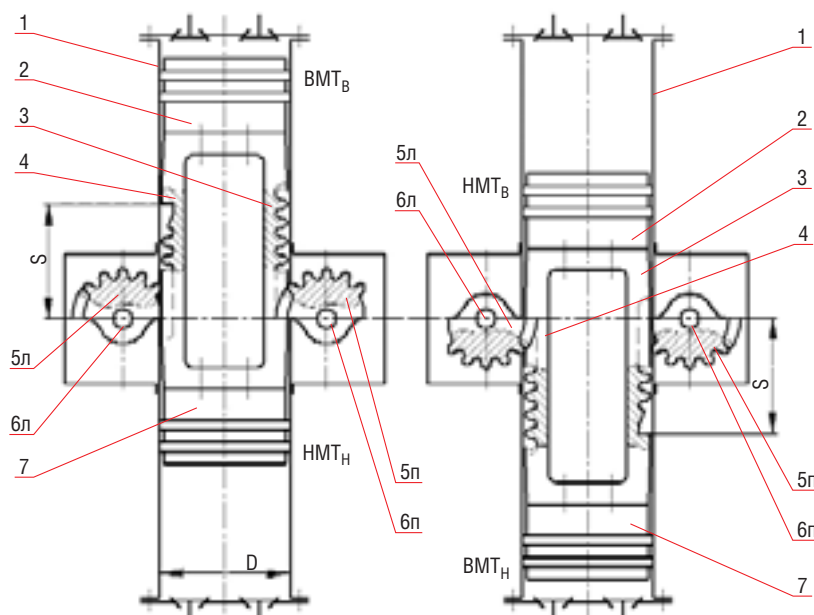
Длинноходный двигатель с БКШМ в двух крайних положениях:
